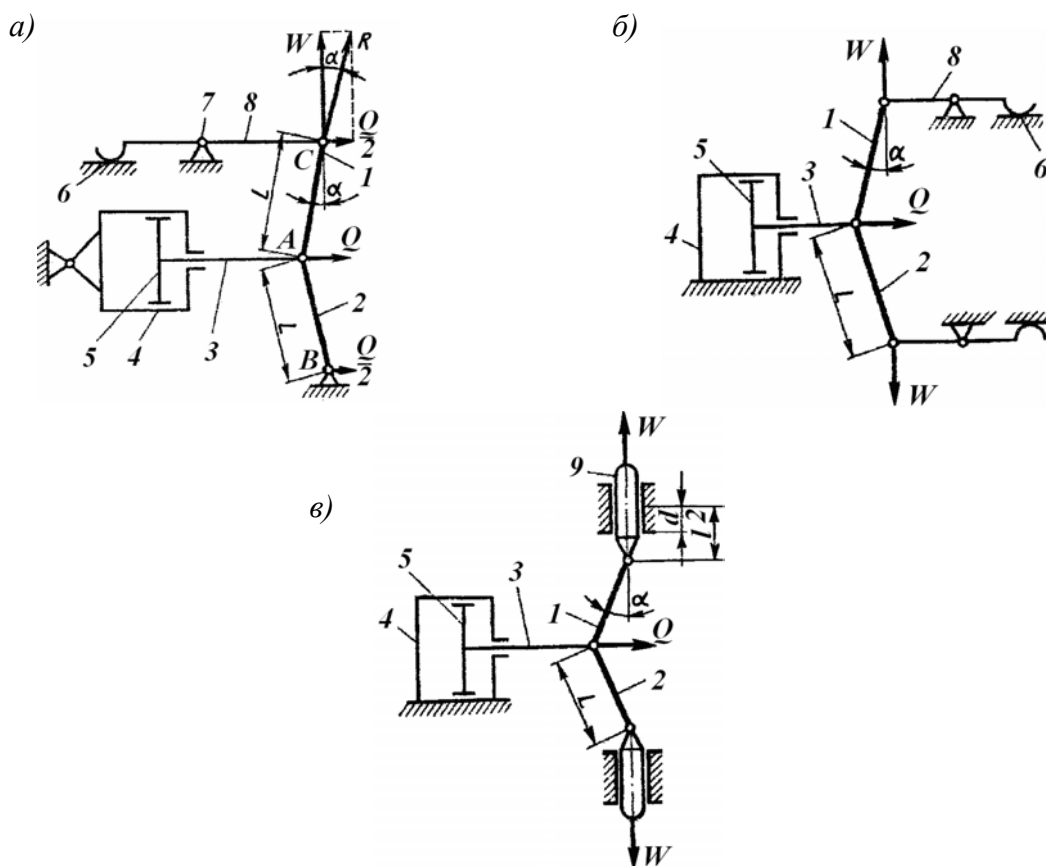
Схемы двухрычажных шарнирных механизмов-усилителей:
